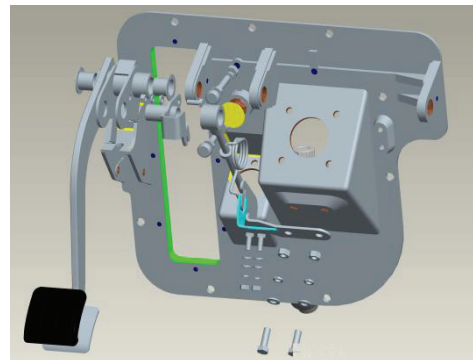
Конструкция кронштейна крепления главного цилиндра
